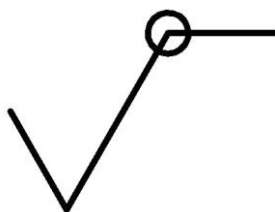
Условный знак обозначения шероховатости по замкнутому контуру
